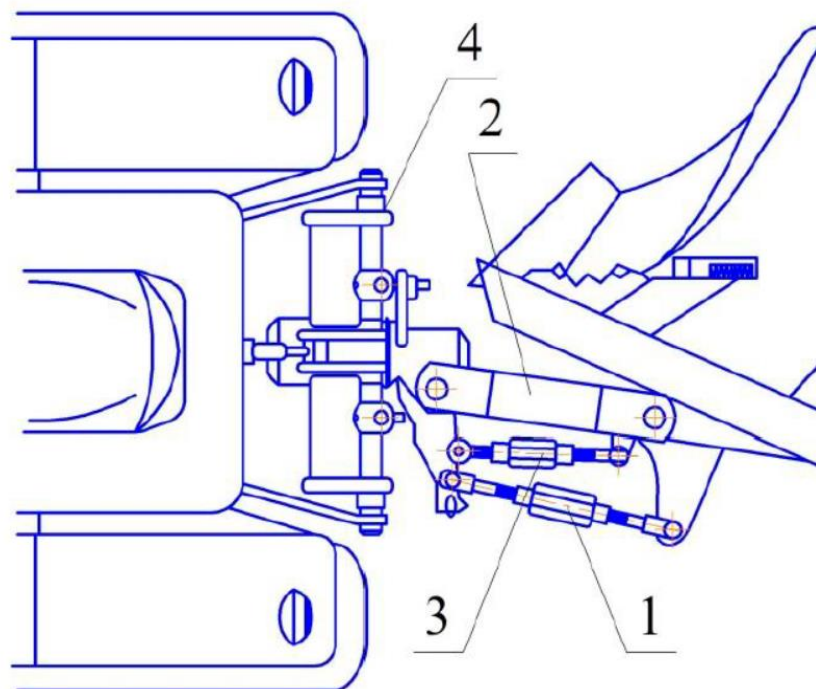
Схема механізмів регулювання лінії тяги та ширини захвату корпусів оборотних плугів: 1 – стяжна муфта регулювання ширини захвату корпусів; 2 – головна тяга рами плуга; 3 – внутрішня стяжна муфта; 4 – палець навіски.
